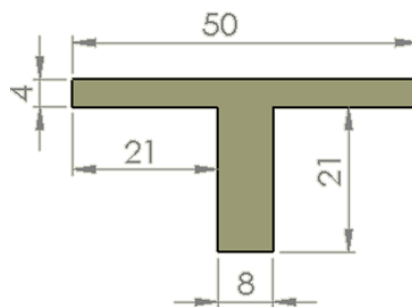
Dimensiones de elemento para porta plantilla.
